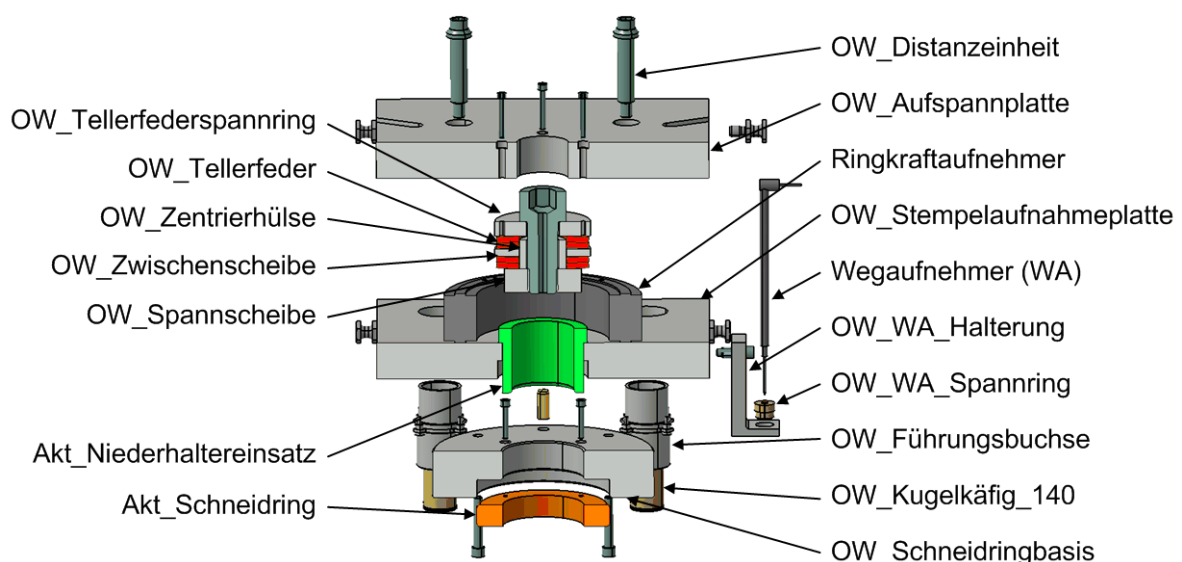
Oberwerkzeug (OW) des Halbwarmschneidwerkzeugs
